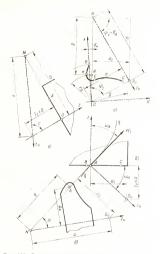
Схема для расчета параметров установки дисковой фрезы для обработки винтовой канавки цилиндрической фрезы
